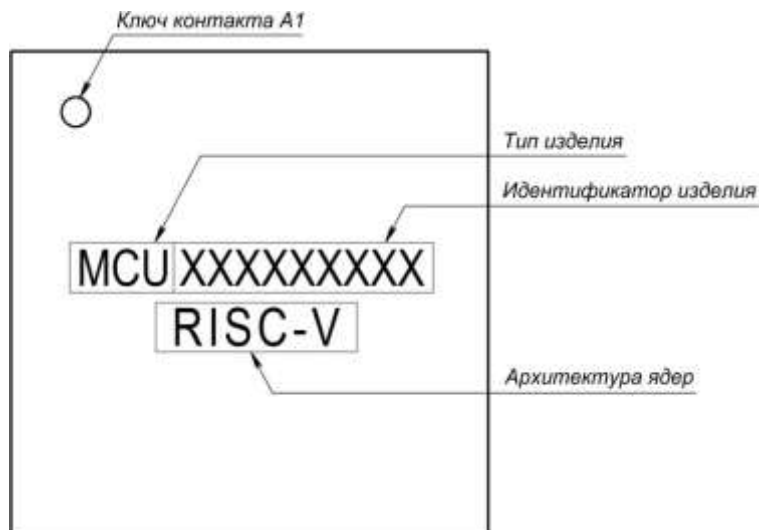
Внешний вид маркировки микроконтроллера
